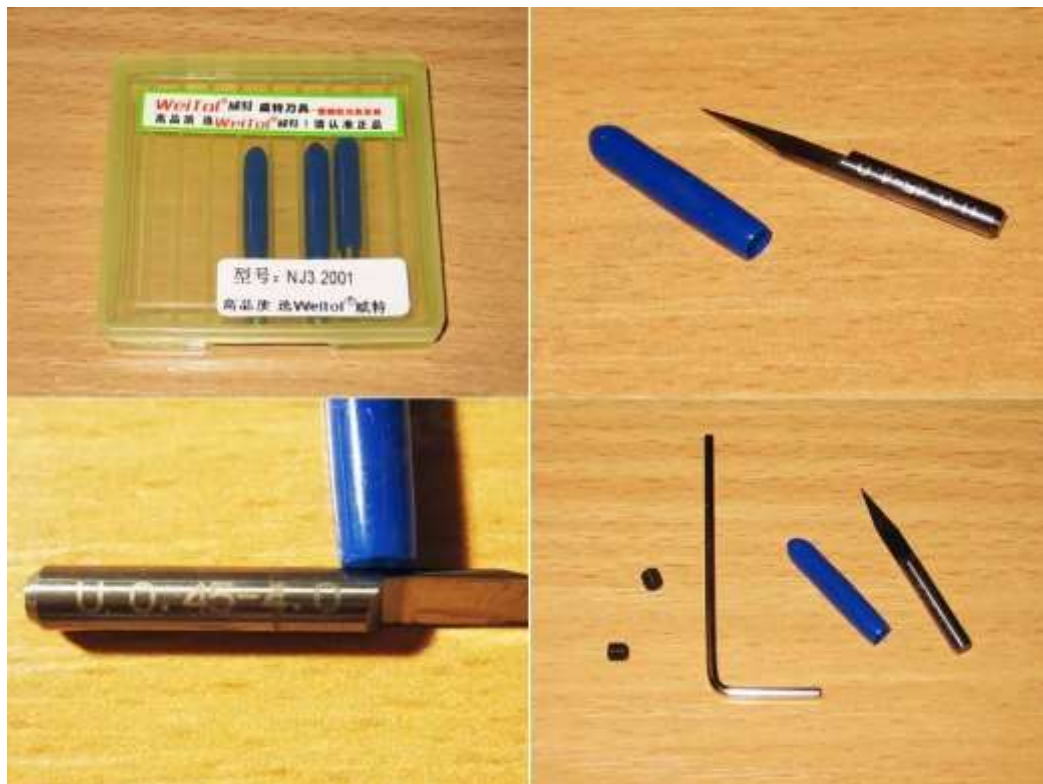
Фреза для фрезерування розробленого макету виробу
